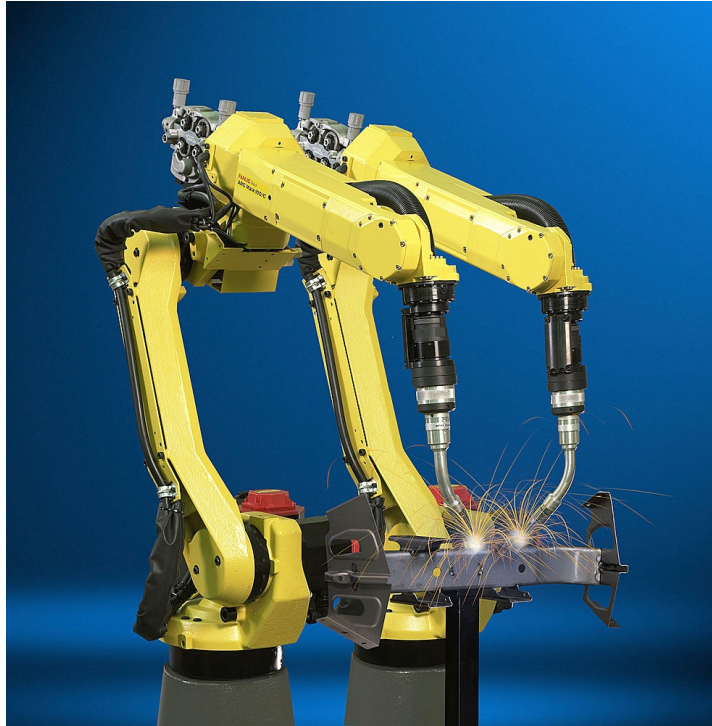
Robot manipulador con elemento terminal para soldadura de arco.
